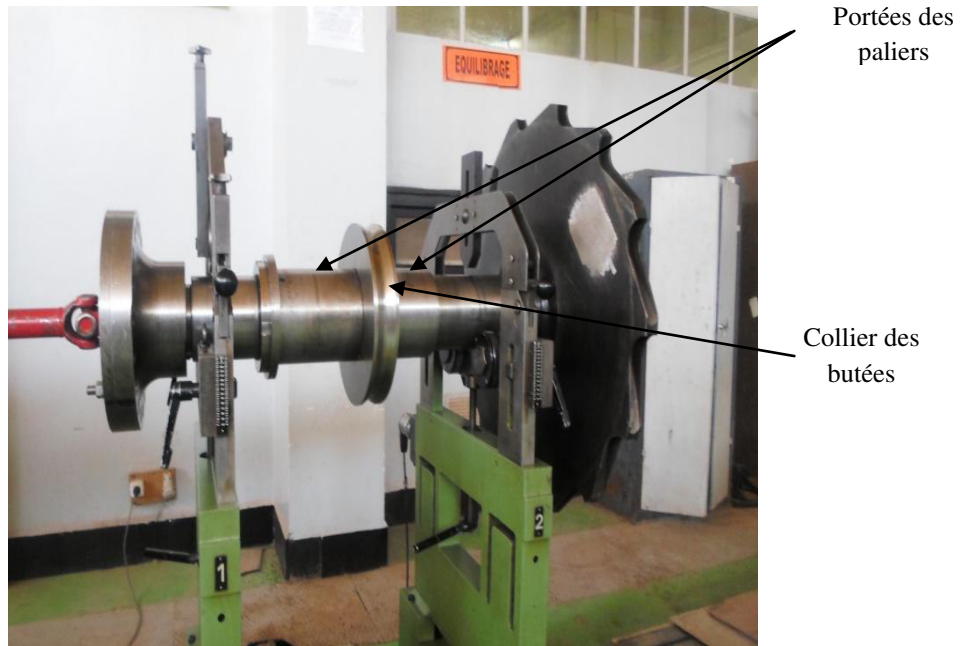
Rotor du compresseur centrifuge Cooper-Bessemer.
